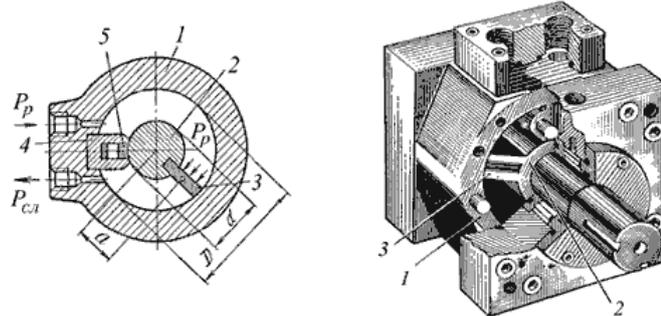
Поворотный однолопастной гидроцилиндр: а - схема; б - общий вид
